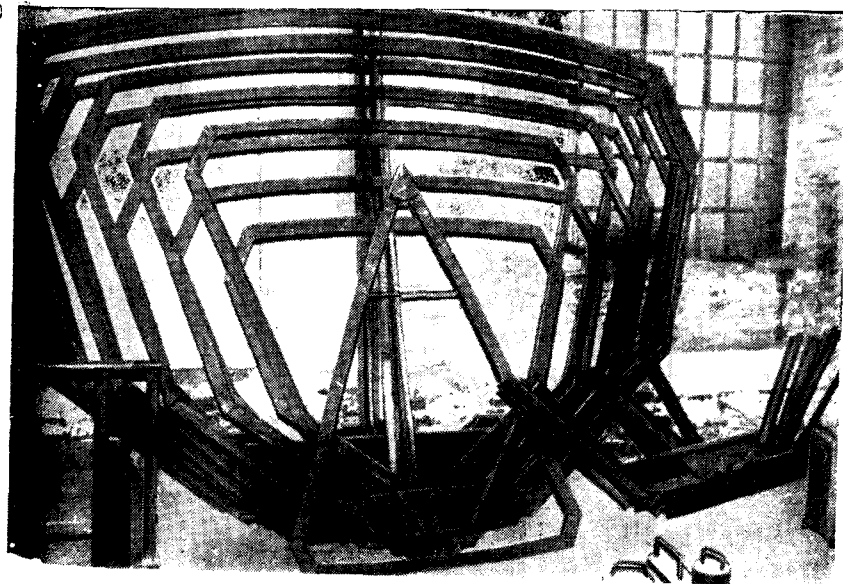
Готовый набор шпангоутов для яхты «Гидра». Не хватает только вырезов для сварных швов в углах рам. На готовых рамах шпангоутов эти вырезы обрабатывают круглым напильником.
